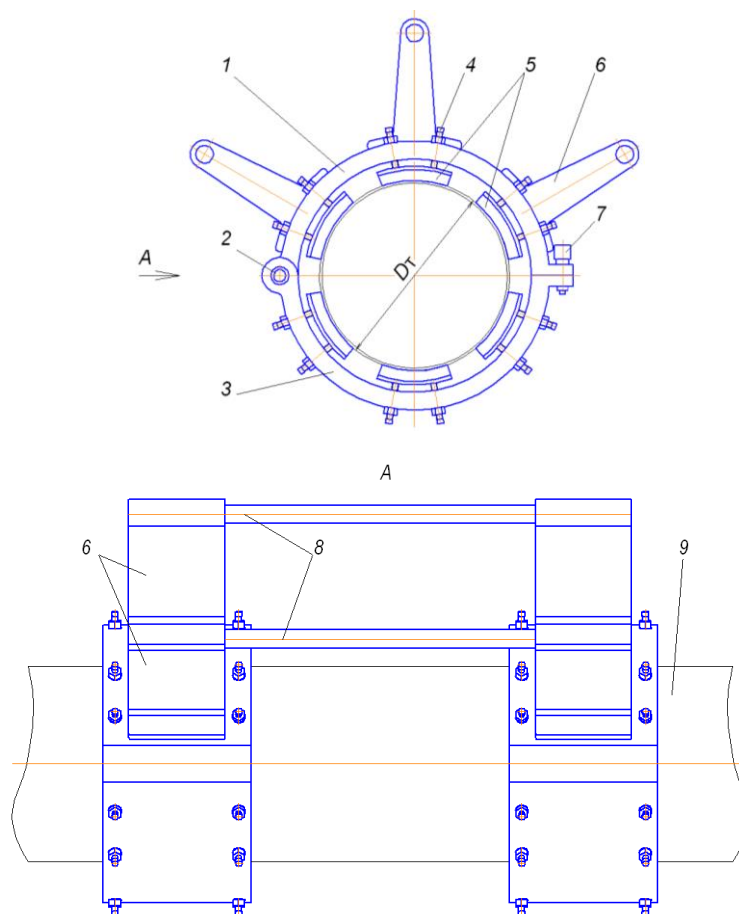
Общий вид предлагаемого центрирующего устройства
